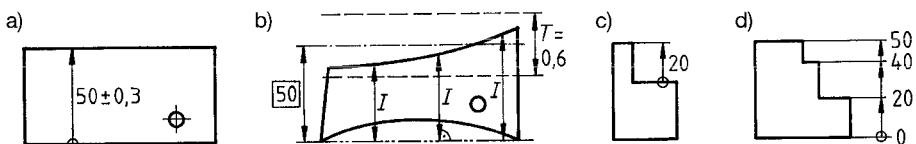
Bezugsbemaßung. a) Zeichnung, b) Prüfung, mit „Toleranzzone“, c) Stufenmaß, d) steigende Bemaßung
